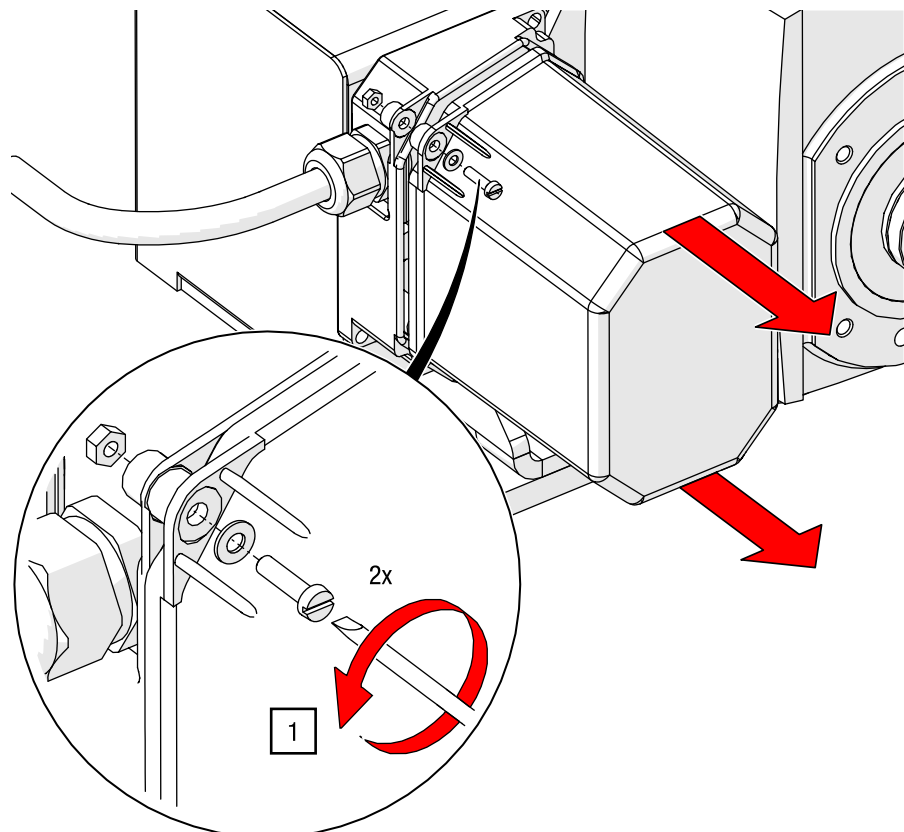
Not-Endschalter einstellen – Einstellschrauben freigeben
